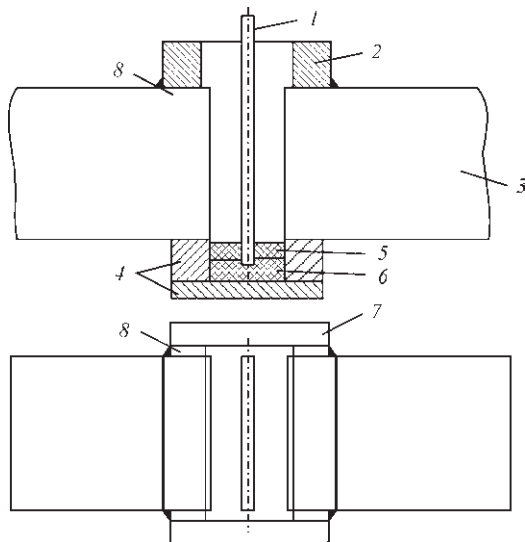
Схема ЭШС: 1 — пластинчатый электрод; 2 — выводные планки; 3 — свариваемый стык; 4 — металлический карман; 5 — рабочий флюс; 6 — экзотермическая смесь; 7 — формирующие подкладки; 8 — боковые планки
